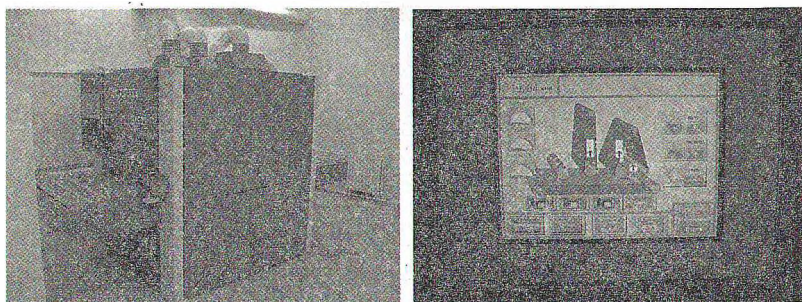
Фрезерно-шлифовальный станок Houfek Bulldog FRC 910
